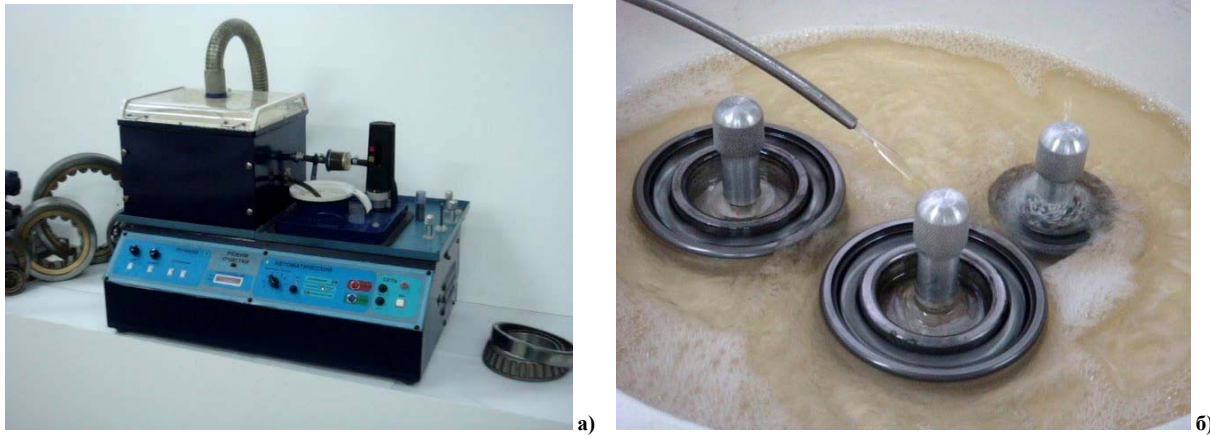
Внешний вид стенда очистки шарикоподшипников ОПШ-01 (а) и камера очистки трех подшипников с разными типоразмерами (б)
